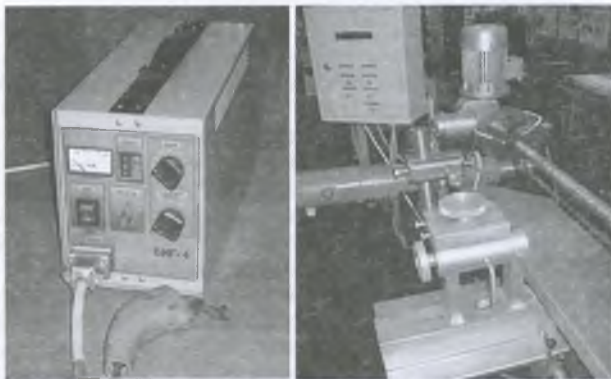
Современное оборудование для ЭИО: а – установка “БИГ-4”; б – вращатель с обрабатываемым устройством.
